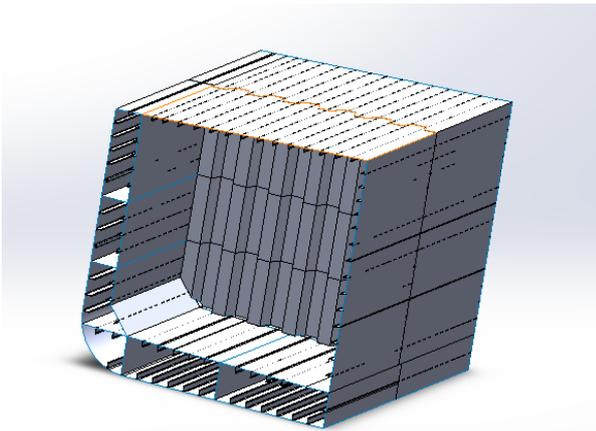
Trapezoid Corrugated Bulkhead Dengan Panjang Elemen 1600
